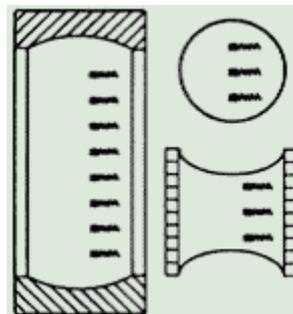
Повреждение подшипника при сборке из-за недостаточного опыта сборки.
